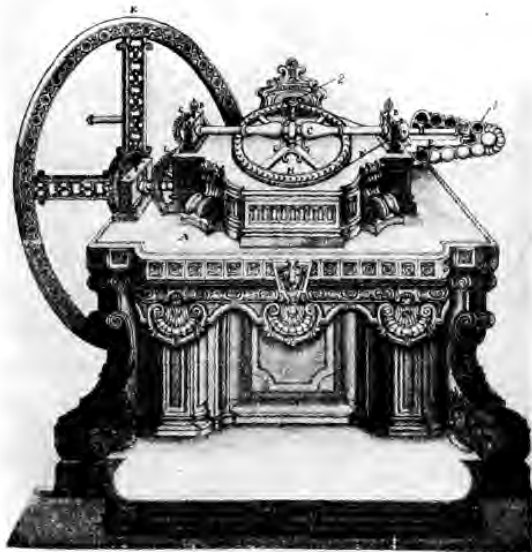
Станок для фрезерования грибовидной фрезой. Рукопись «Театрум Махинарум» А. К. Нартова.
